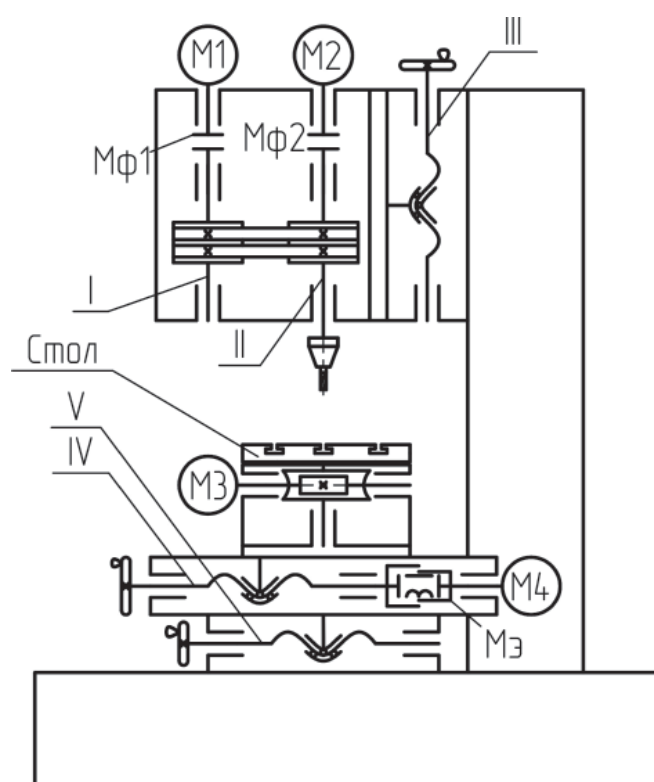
Кинематическая схема станка с двумя приводами вращения инструмента:
